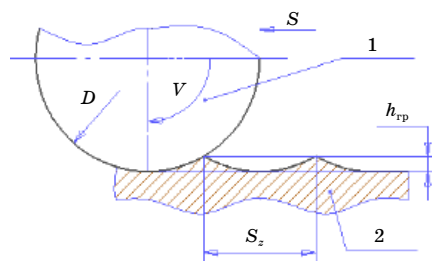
Параметры поверхности при контурном фрезеровании изделия концевой фрезой диаметром  $D$ : 1 — фреза; 2 — обрабатываемое изделие
